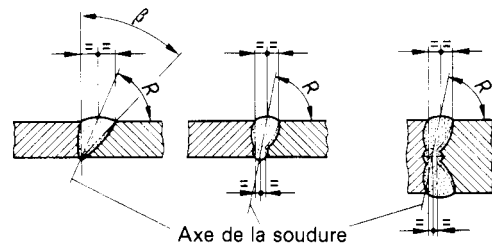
Exemples de rotation, R , des soudures bout à bout asymétriques sur surface de pièce horizontale
